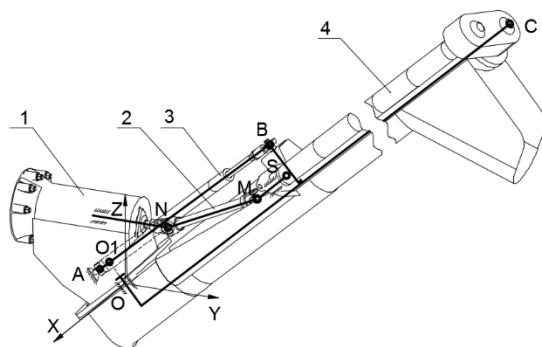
Схема механизма поворота шнека с наложенными связями
